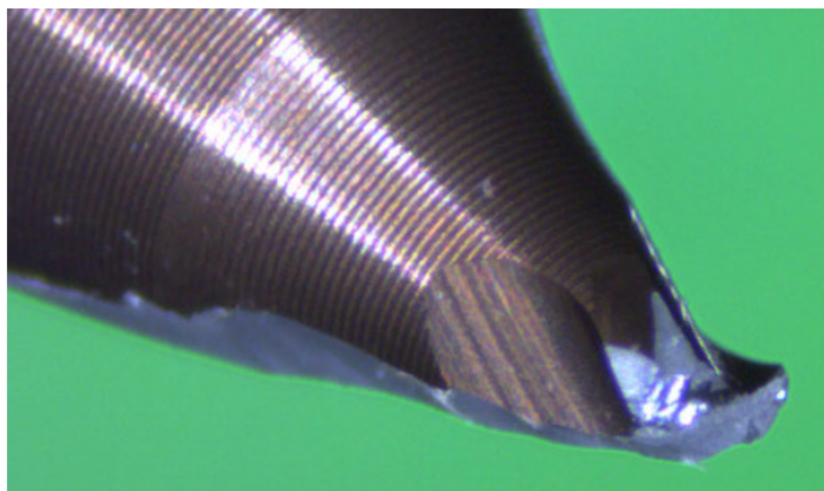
Fräs Werkzeug 0 nach der Bearbeitung
